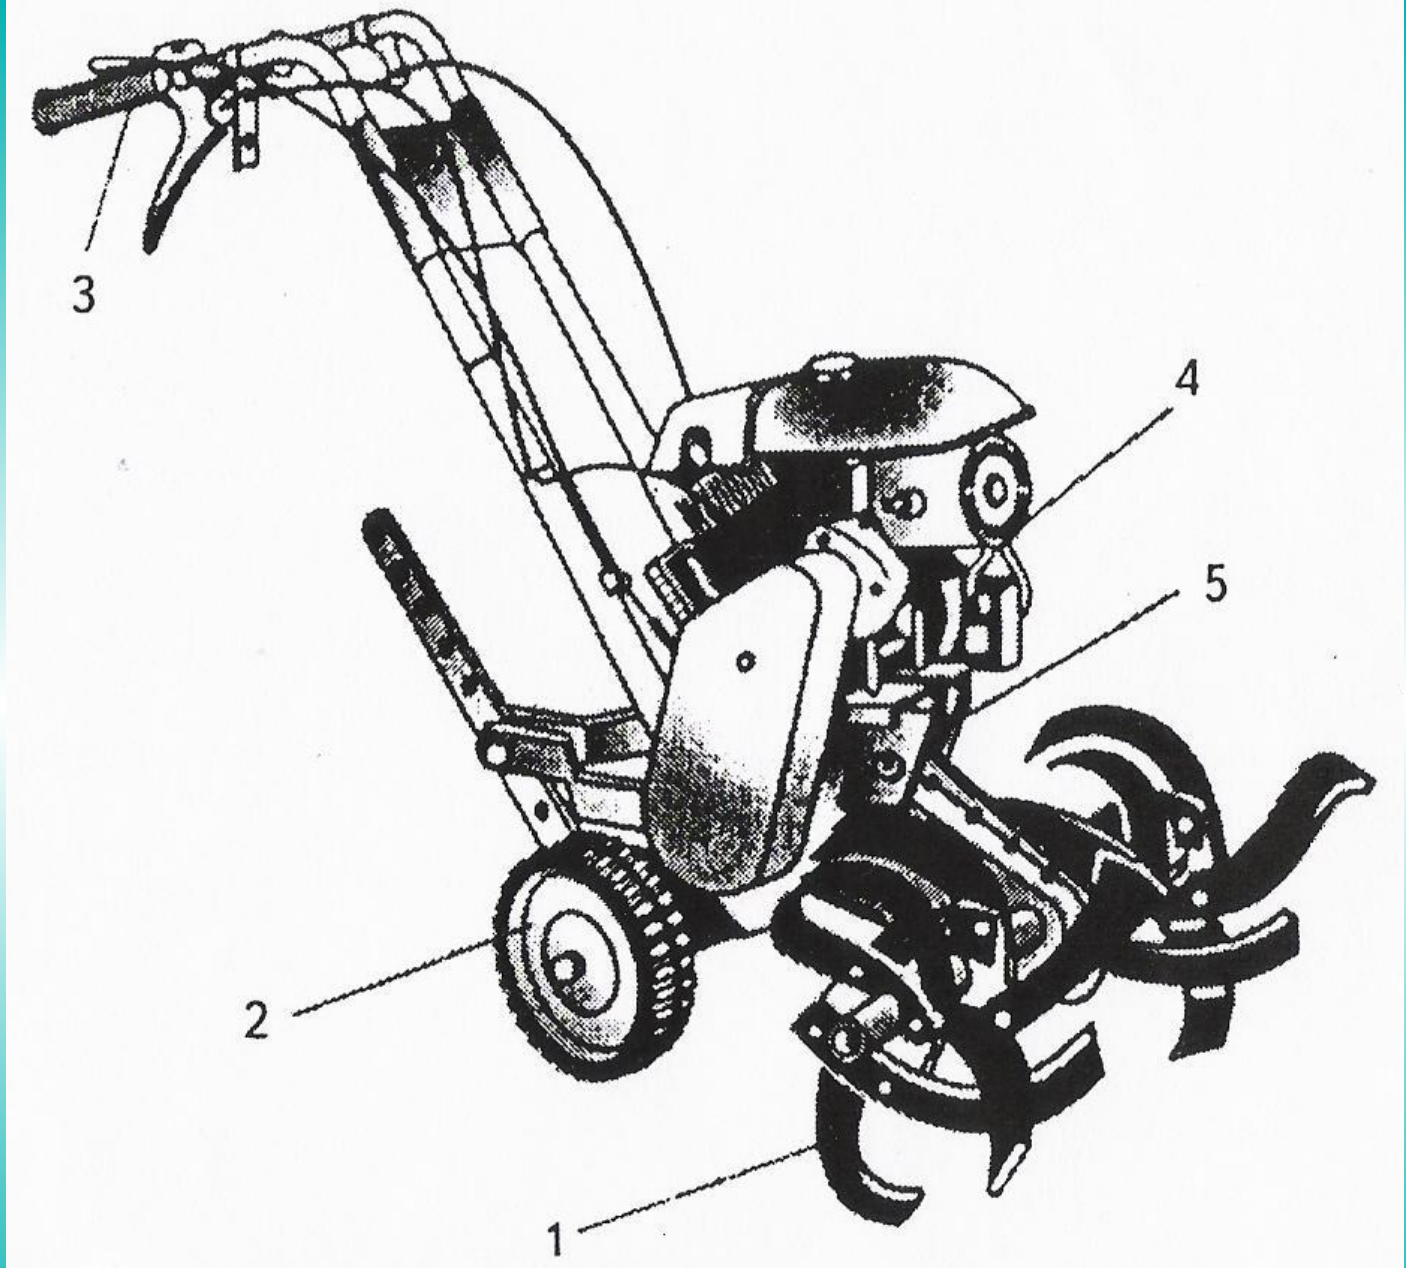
Мотофреза МК-1 «Крот»: 1 – фреза; 2 – ходовые колеса; 3 – рукоятка управления; 4 – двигатель; 5 – рама
